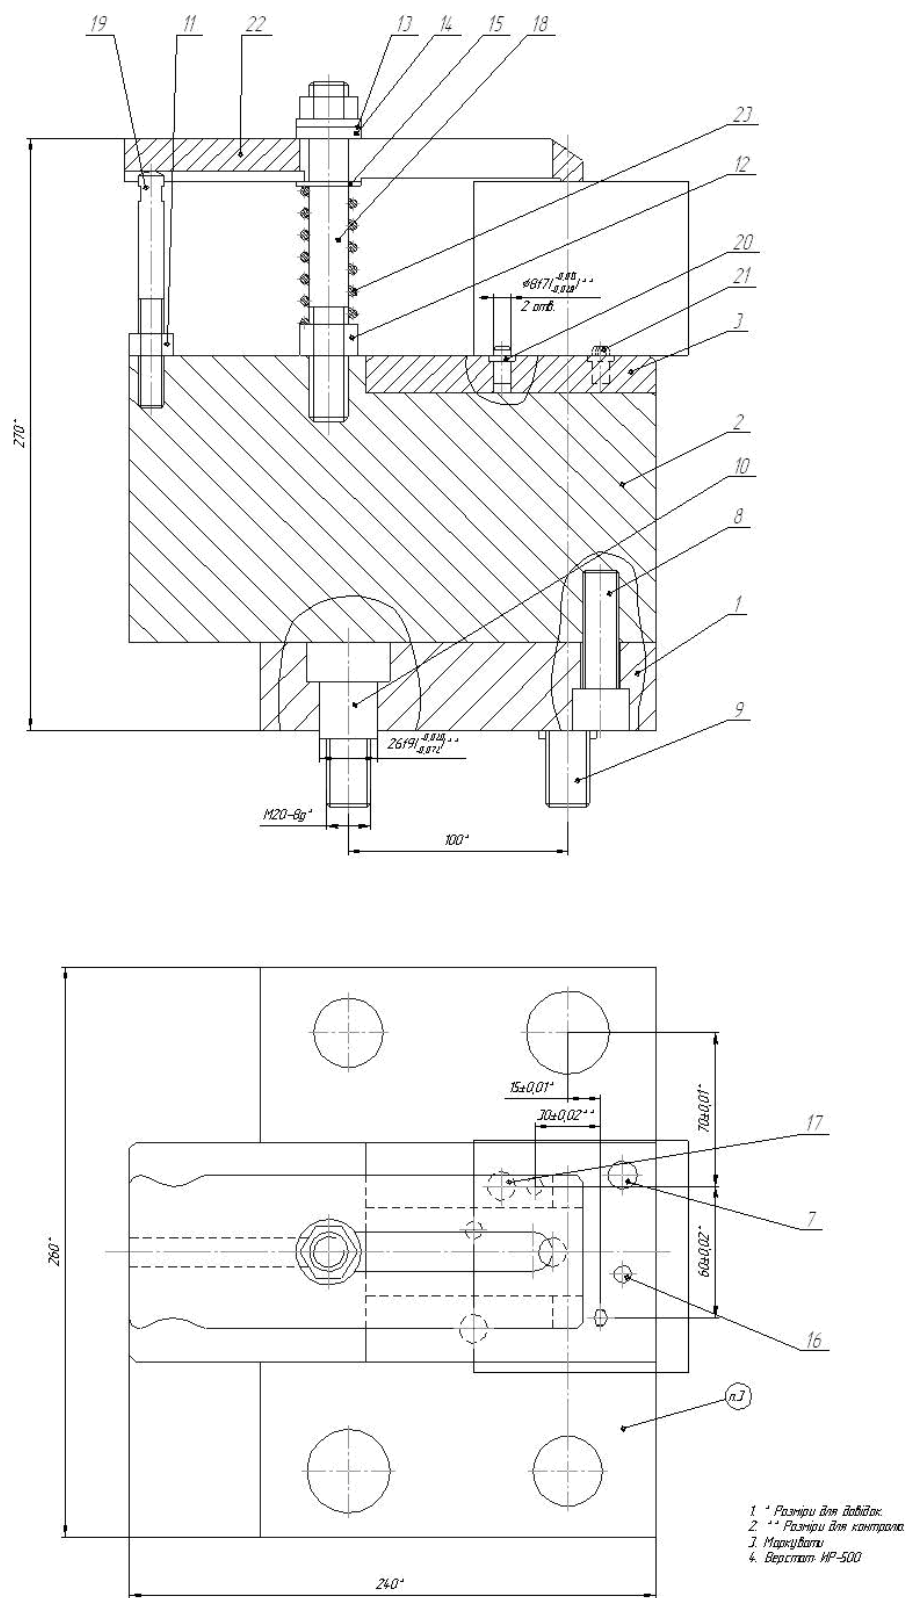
Пристосування для фрезерування з установкою заготовки на два пальця
